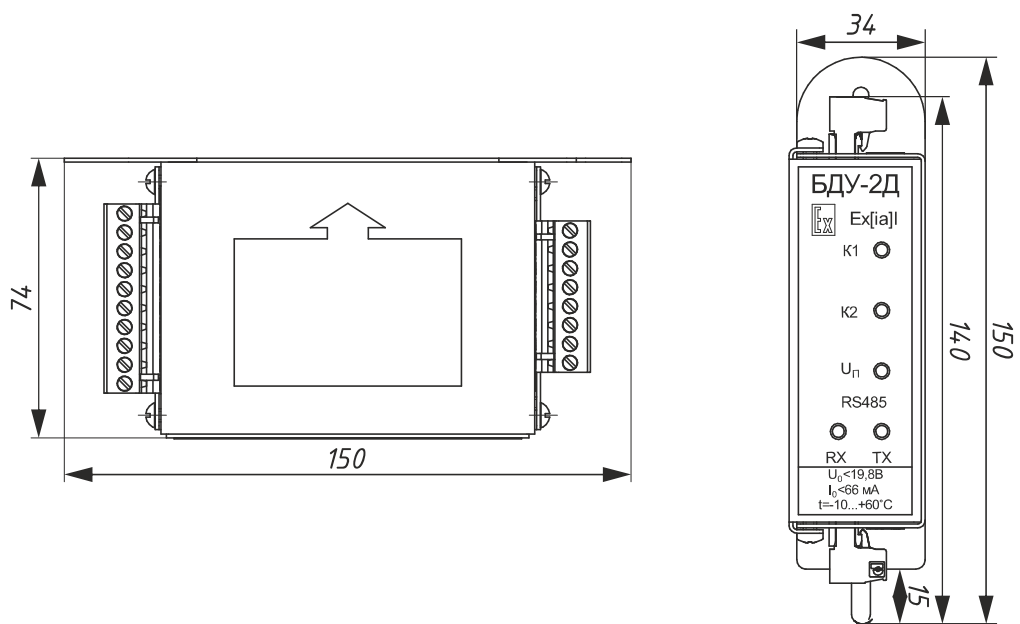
Габаритные размеры второго типа корпуса блока БДУ-хД.2хх
